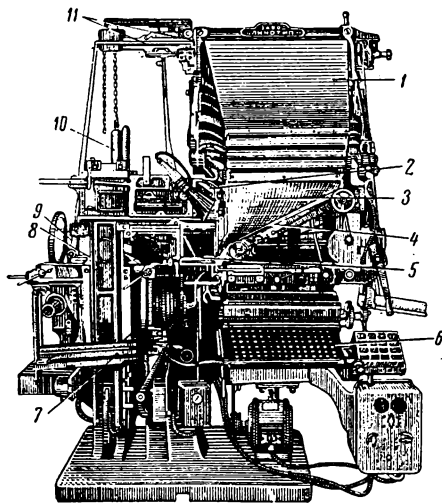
Технический рисунок (общий вид линотипа: 1 — магазины с матрицами; 2 — коробка с клиньями; 3 — направляющие ребра собирателя; 4 — транспортер матриц; 5 — верстатка; 6 — клавиатура; 7 — столик для отличных строк; 8 — отливная форма; 9 — котел с расплавленным металлом; 10 — металл для отливки строк; 11 — аппарат для разбора матриц)
